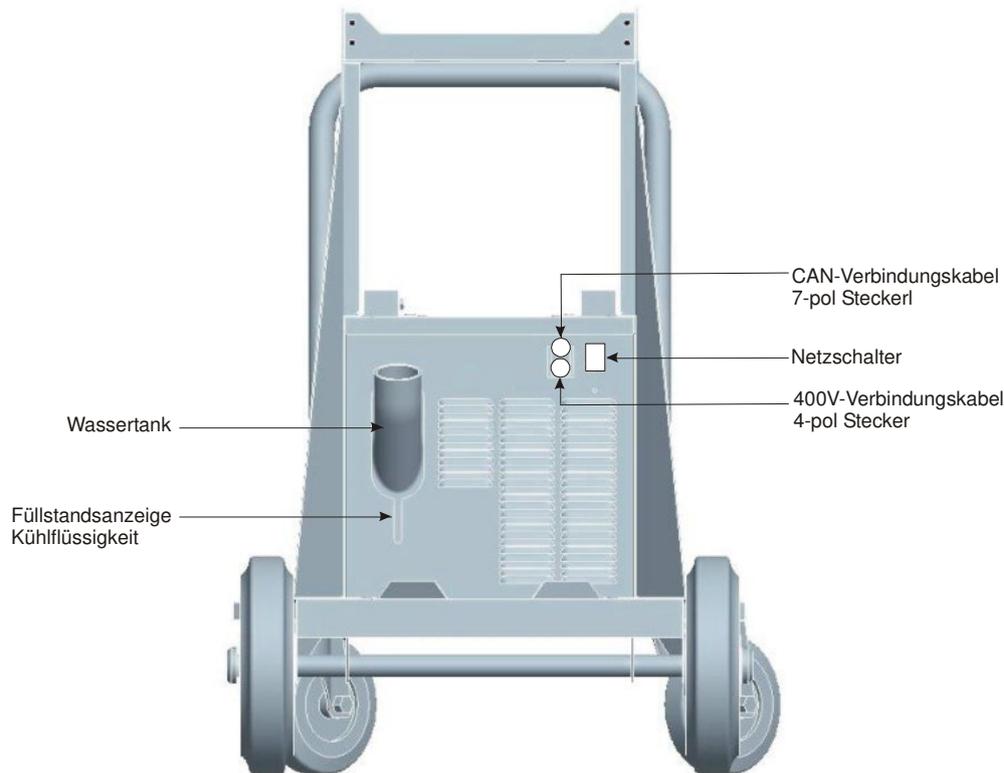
TIG - COOL CART 2000 Ansicht von Hinten
